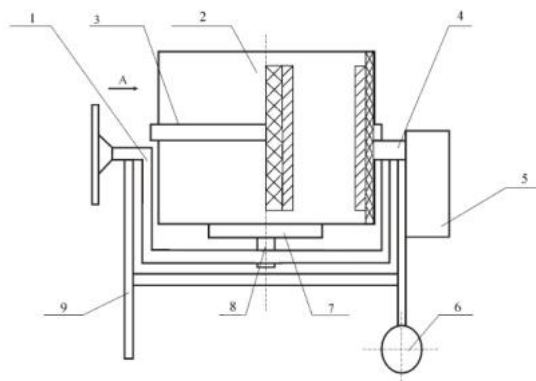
Фронтальний розріз установки магнітної обробки бульб картоплі.
